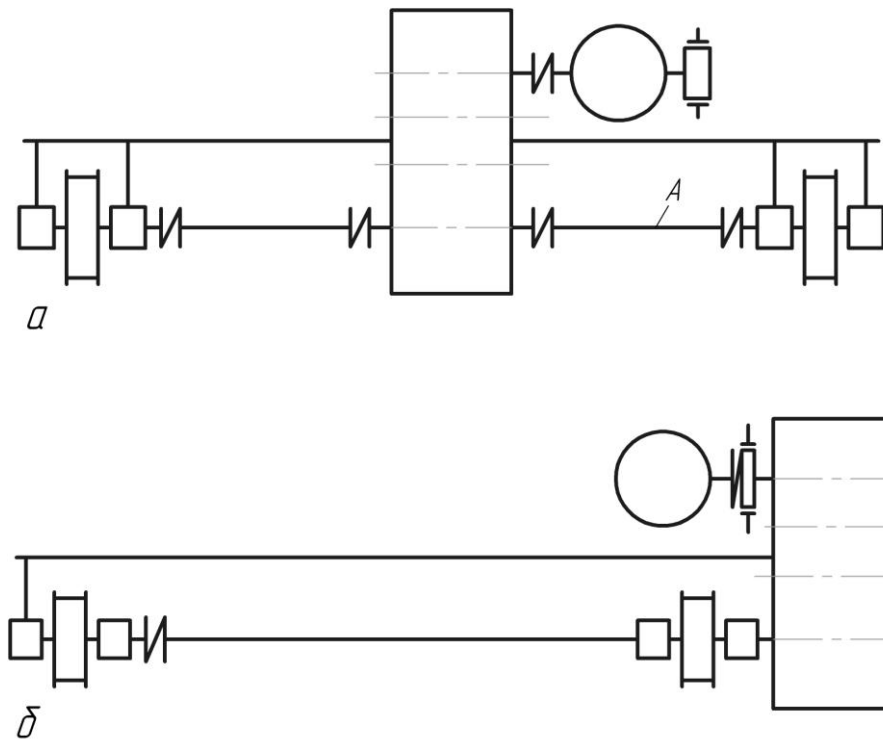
Схема механізмів пересування візка мостового крана: із центральним розташуванням вертикального кранового редуктора типу ВК (а) і з консольним редуктором типу ВКН. А – проміжний вал.
